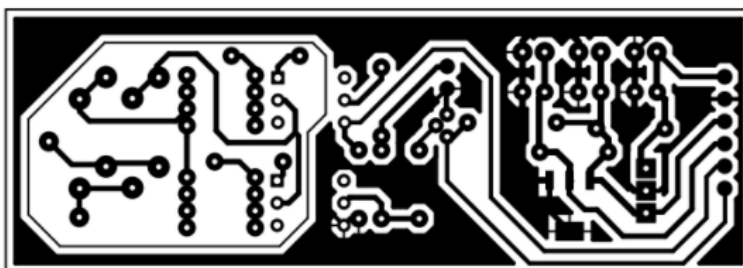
Plantilla PCB para la placa de prueba 2.
